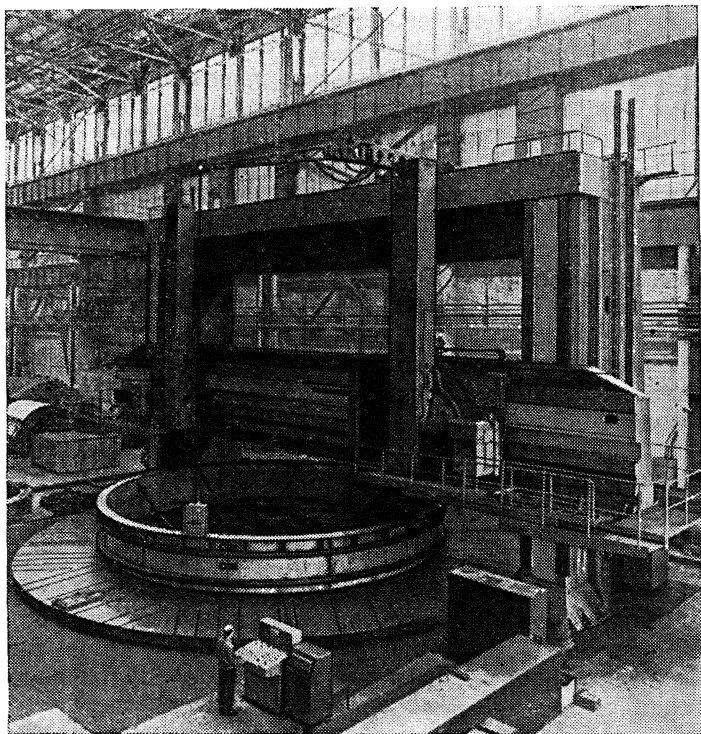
Уникальный токарно-карусельный двухстоечный универсальный станок мод. 1А594
